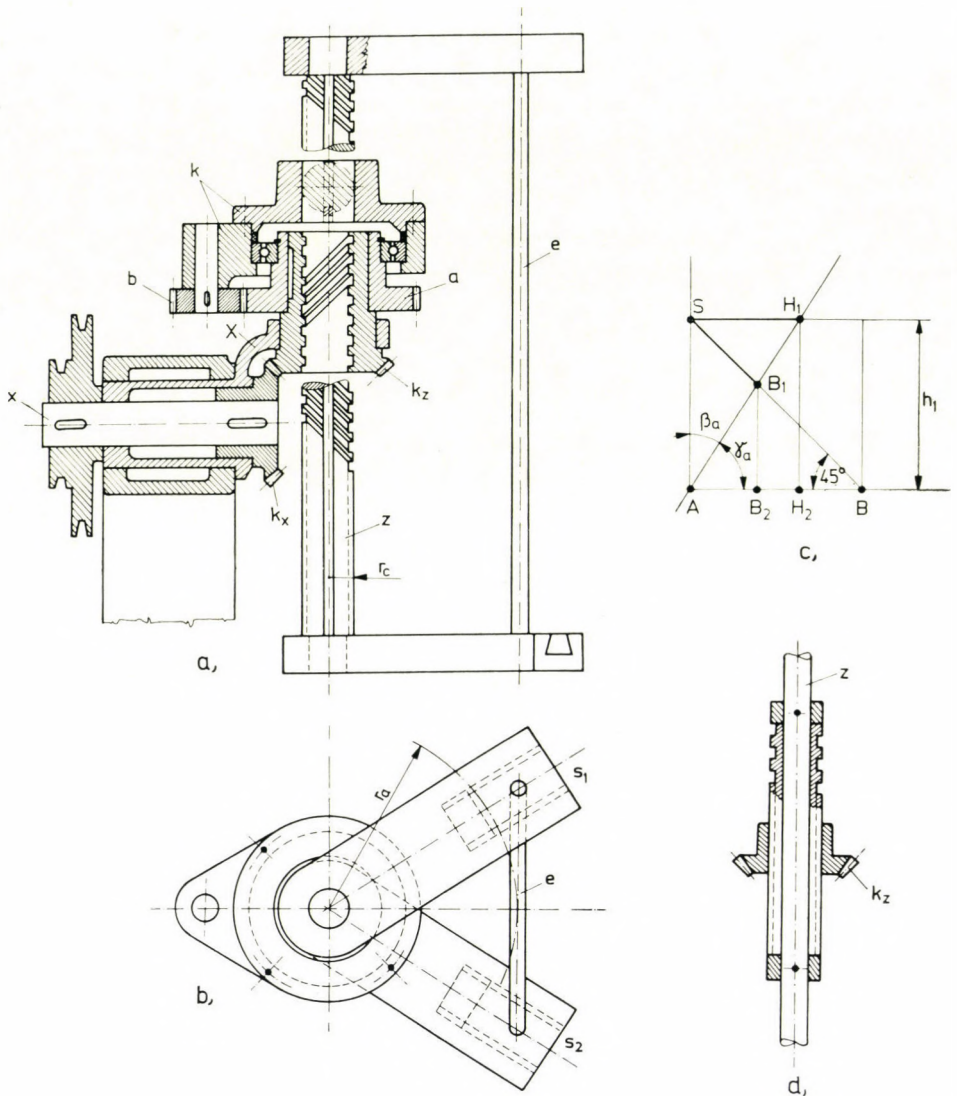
Zusammenstellung der Gewindespindel-Vorrichtung. Seitenansicht
